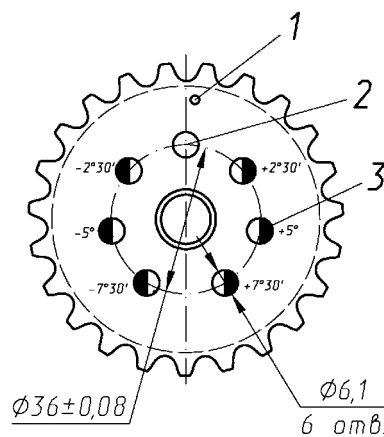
Звездочка распределительного вала с дополнительными отверстиями:
